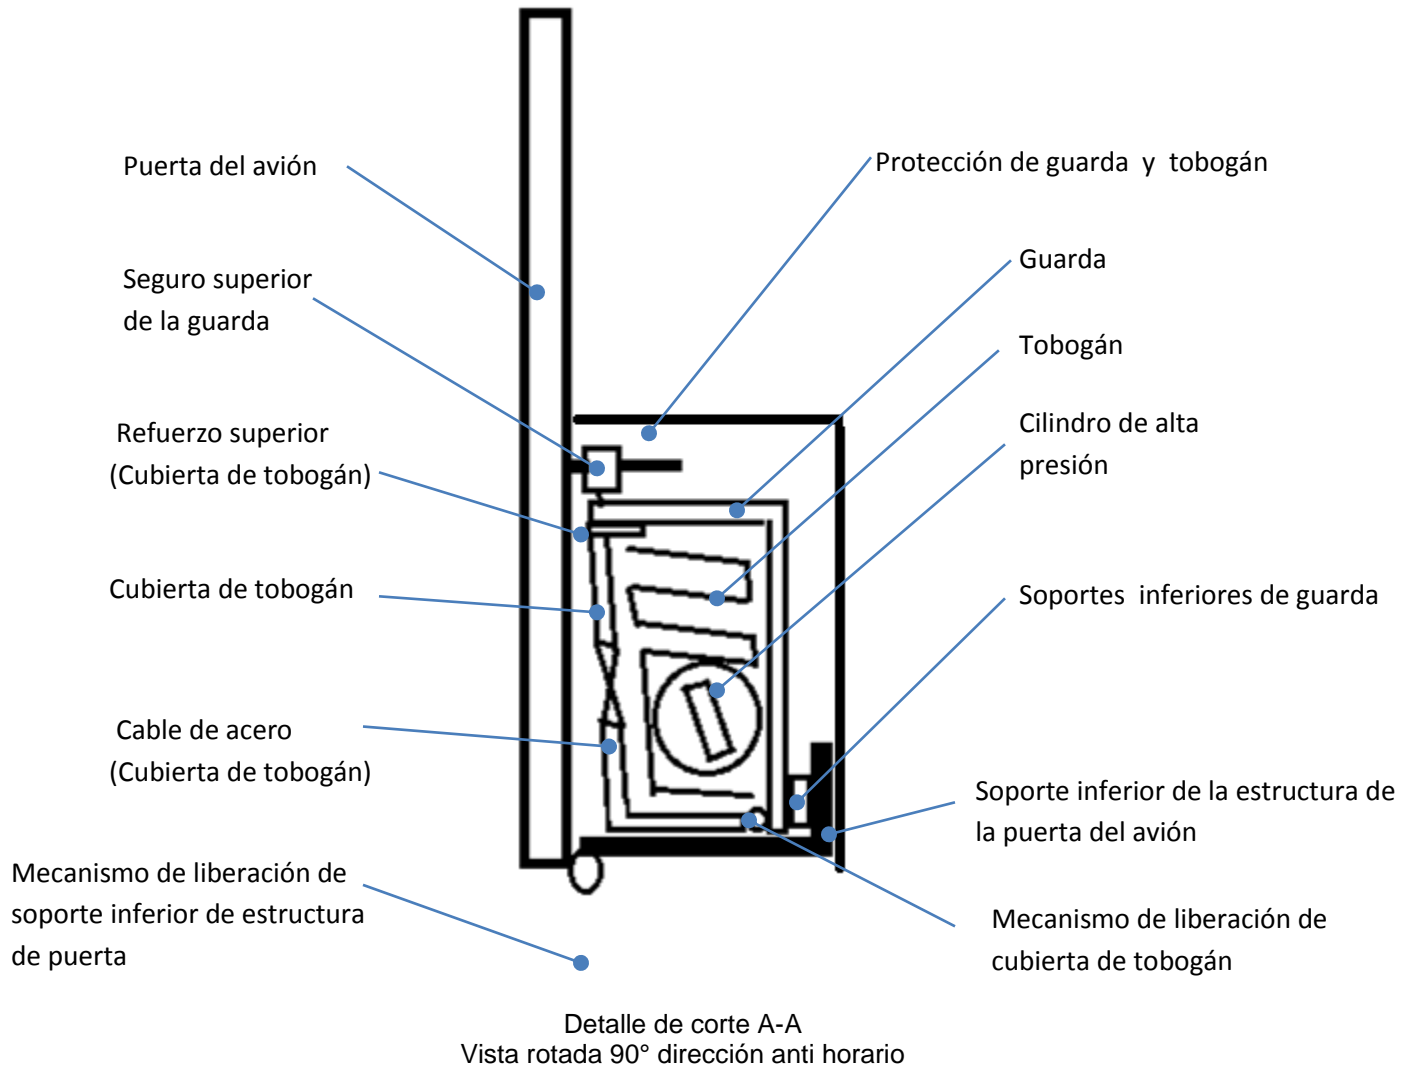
Corte de ensamble del sistema de salida de emergencia con puerta abierta
